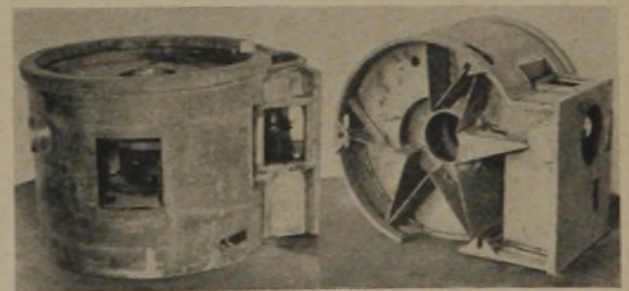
Bett einer Karussell-Drehbank (Stahlbau)
